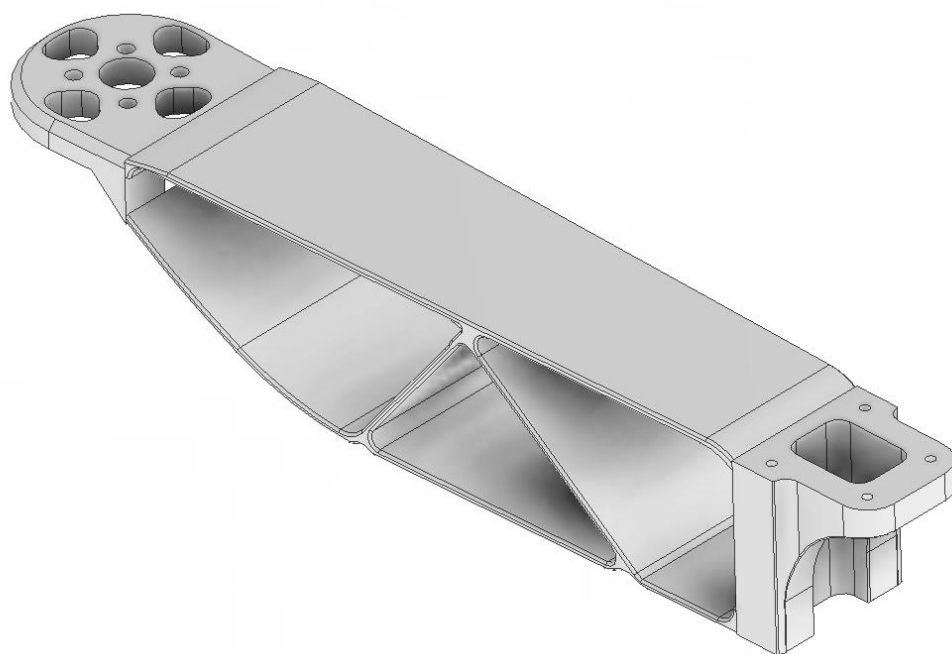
Finální CAD model návrhu s omezením Single draw -Z
